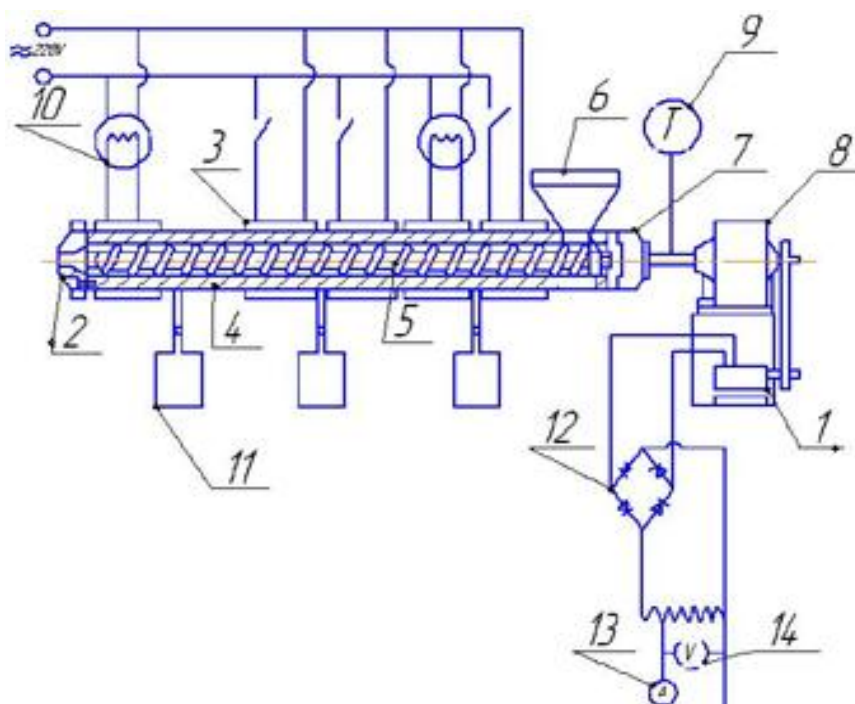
Схема лабораторной установки одношнекового горизонтального экструдера полимеров: 1 - двигатель; 2 - экструзионная головка; 3- нагреватель корпуса; 4 - корпус; 5 - шнек; 6 - загрузочное устройство; 7 - упорный подшипник; 8- редуктор; 9 - тахометр; 10 - регулятор напряжения; 11 - мультиметр для измерения температуры; 12 - выпрямитель; 13 - амперметр; 14 – вольтметр
